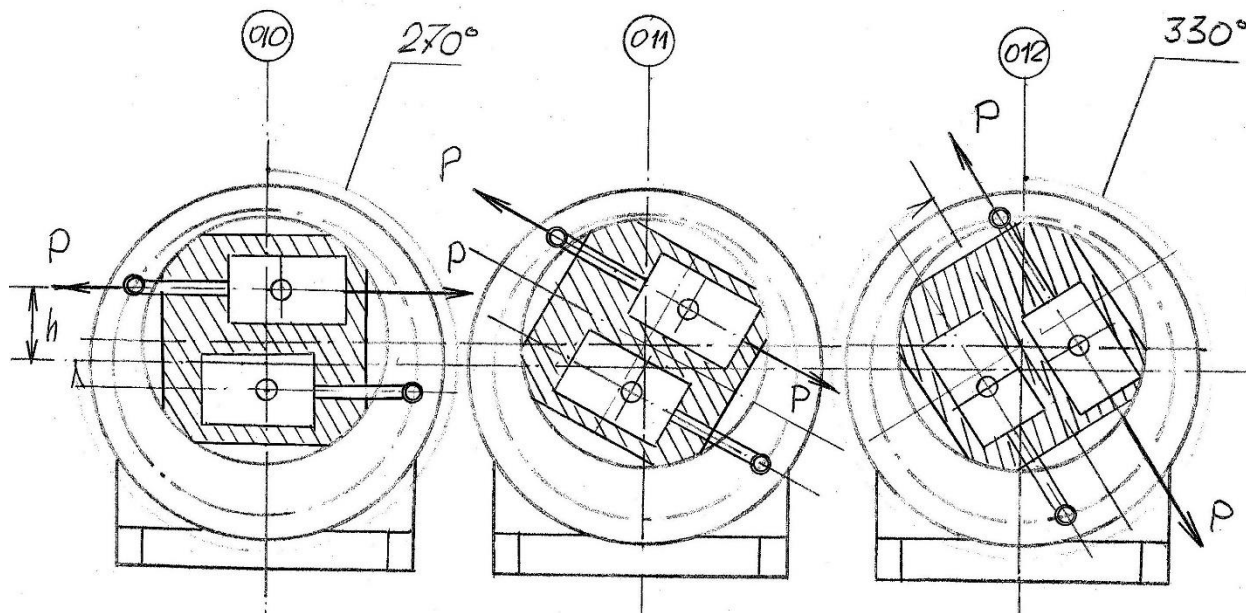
Чертёж позиций поршней и цилиндров роторного двигателя в процессе вращения
